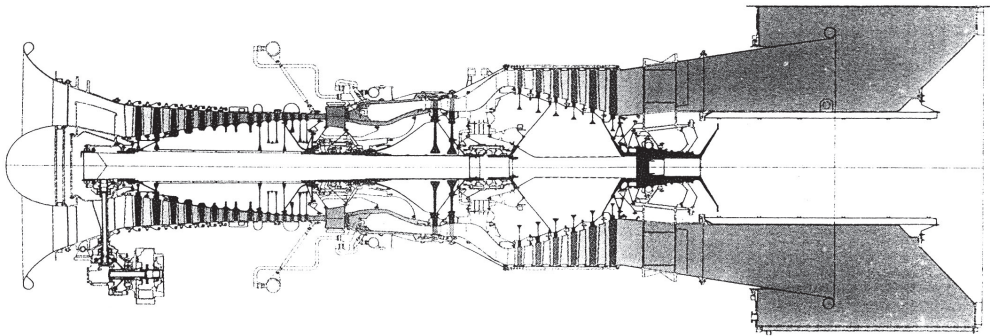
Продольный разрез двигателя LM2500 GE
